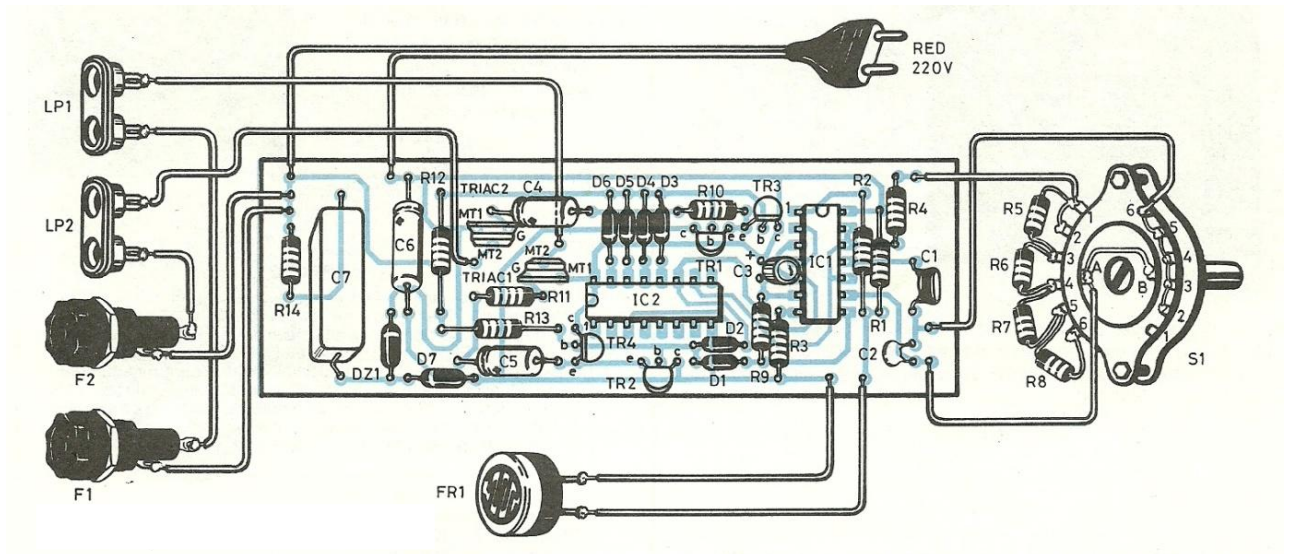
Montaje de todos los componentes en la placa de circuito impreso.
